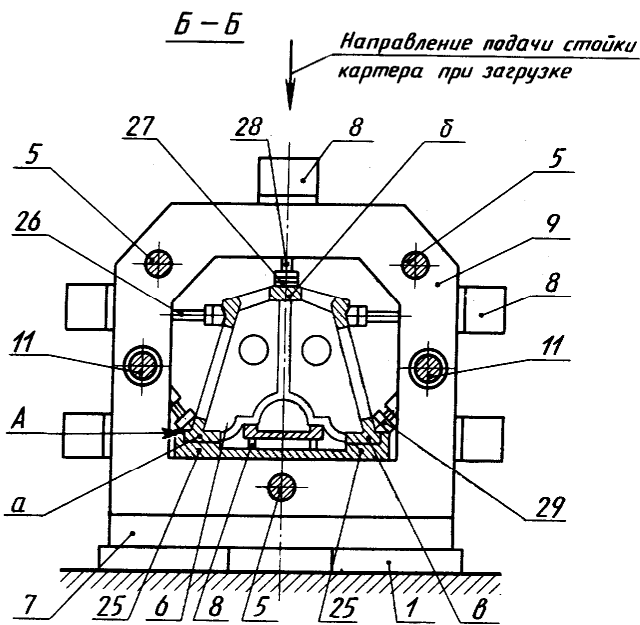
Конструкция установки для контактной стыковой сварки блока цилиндров
